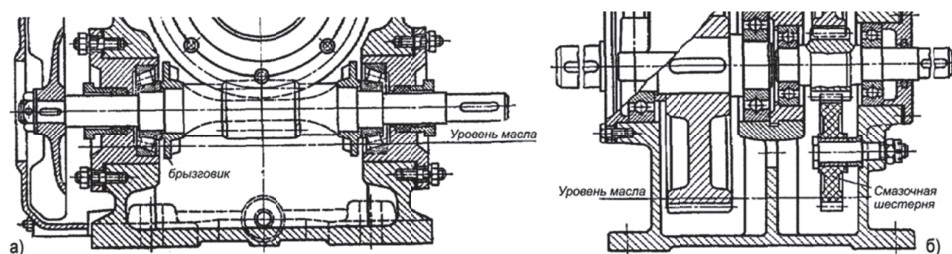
Редукторы червячный и цилиндрический зубчатый со смазочной шестерней
